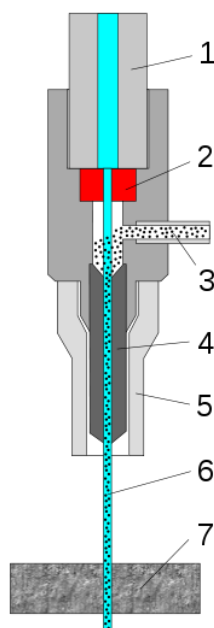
Схема установки гидроабразивной резки.
